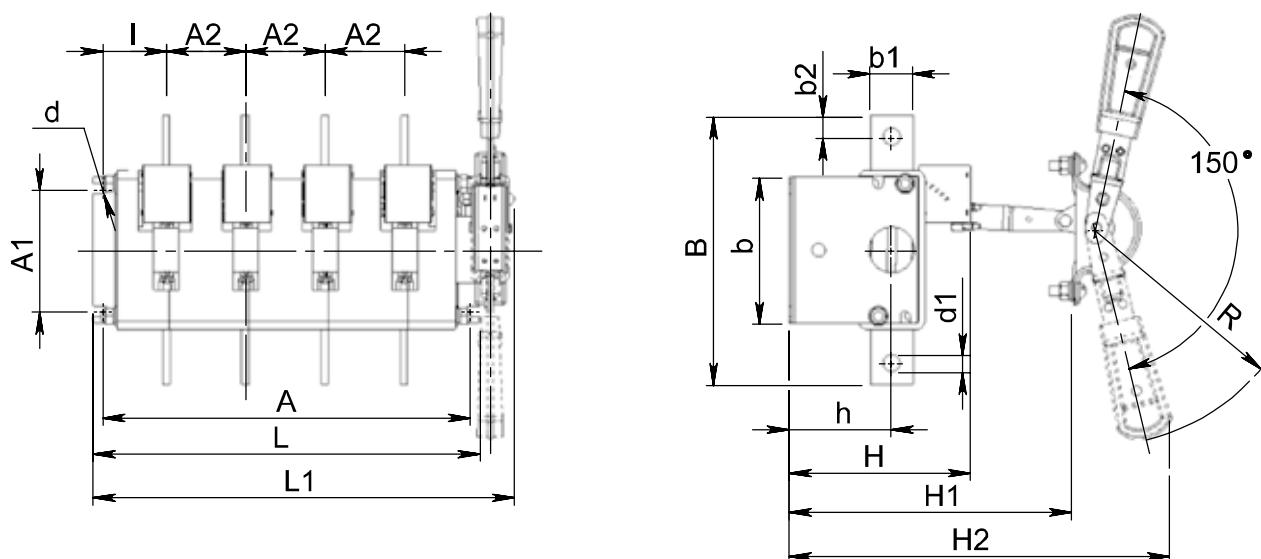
Выключатель-разъединитель на одно направление 4-полюсный с передней смещенной рукояткой
